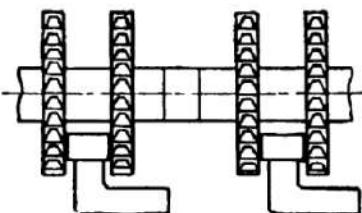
Набор фрез для обработки пазов, уступов (сбоку) и площадки.
